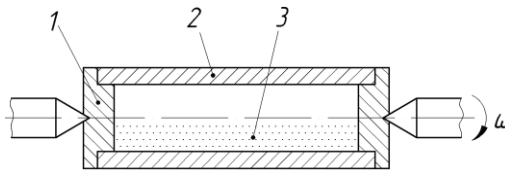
Схема нанесення евтектичного покриття на внутрішню поверхню циліндричних деталей: 1 – ущільнювальний фланець, 2 – втулка, 3 – порошкова суміш
